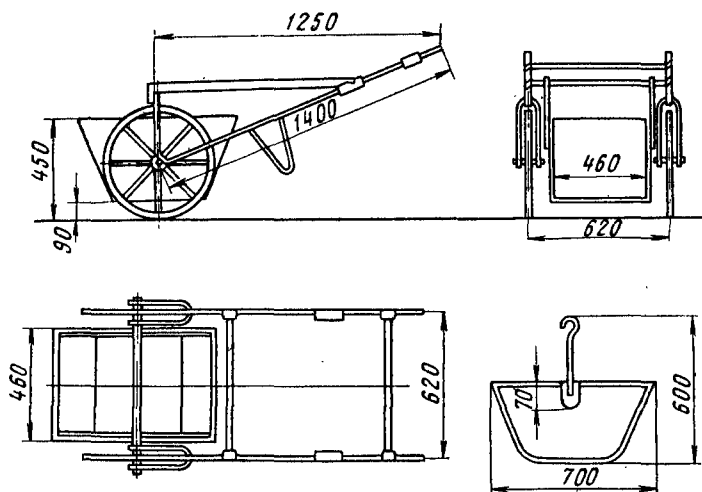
Двухколесная металлическая тачка для перевозки растворов
